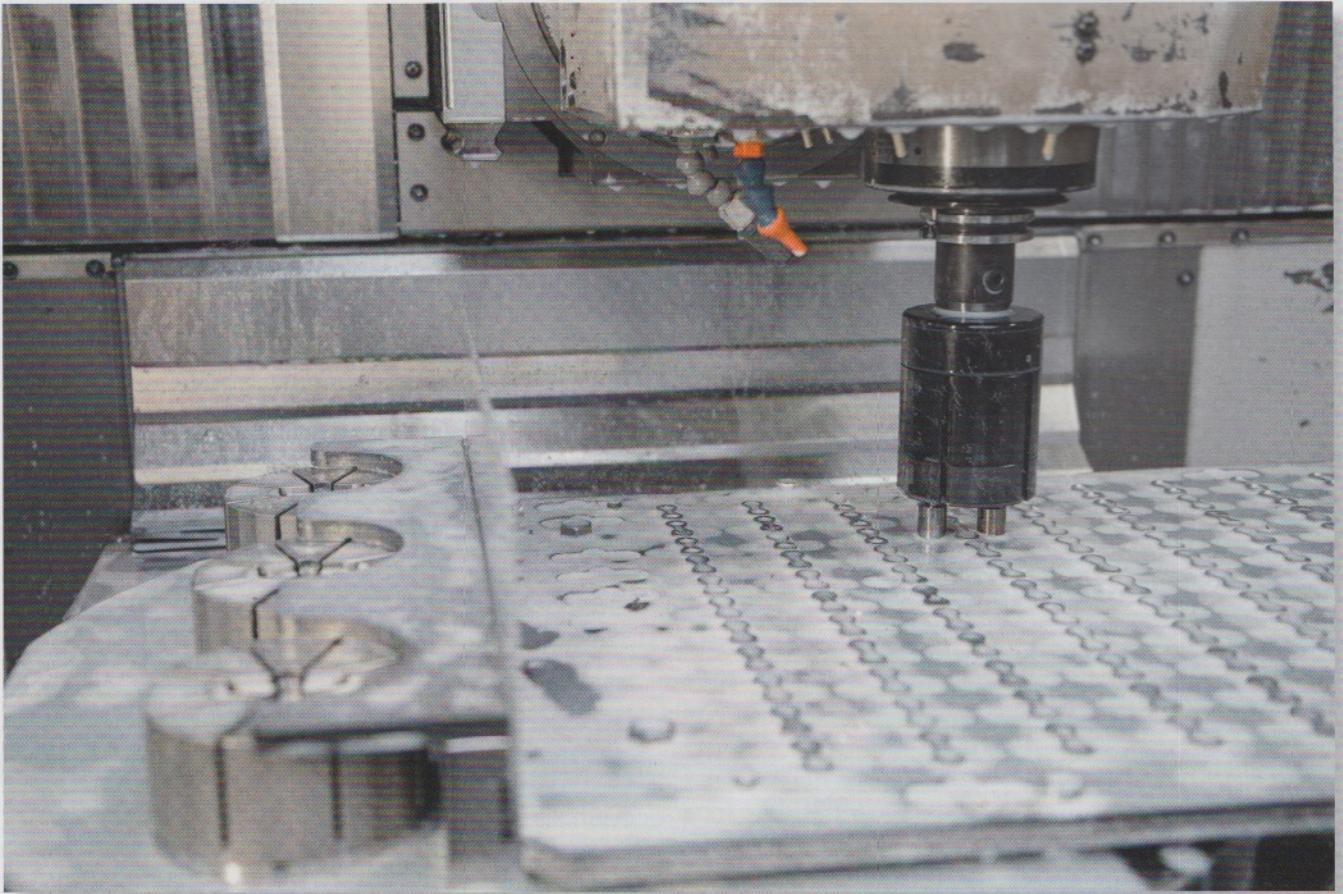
Das neue Greifsystem hat eine Schaftschnittstelle und wird wie ein Werkzeug eingewechselt. Anwender realisieren damit den vollautomatischen Werkstückwechsel während der Bearbeitung auf einer Werkzeugmaschine
